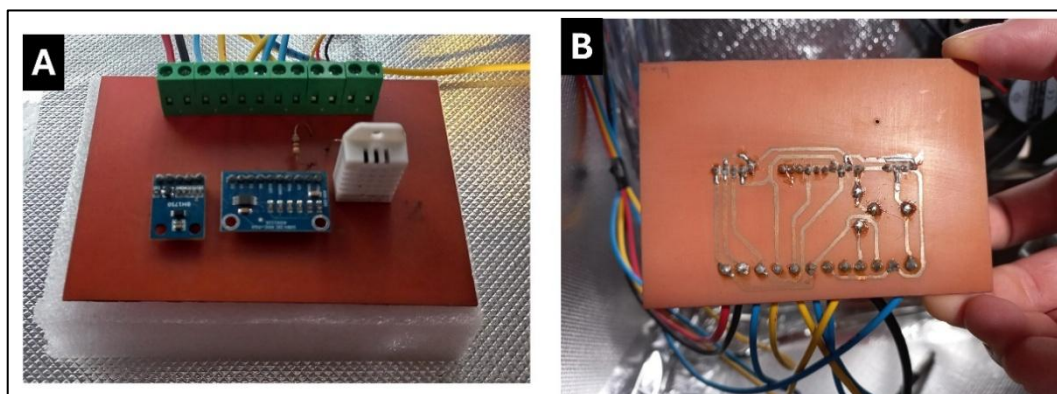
A) Vista superior da PCB projetada; B) Vista inferior da PCB projetada
